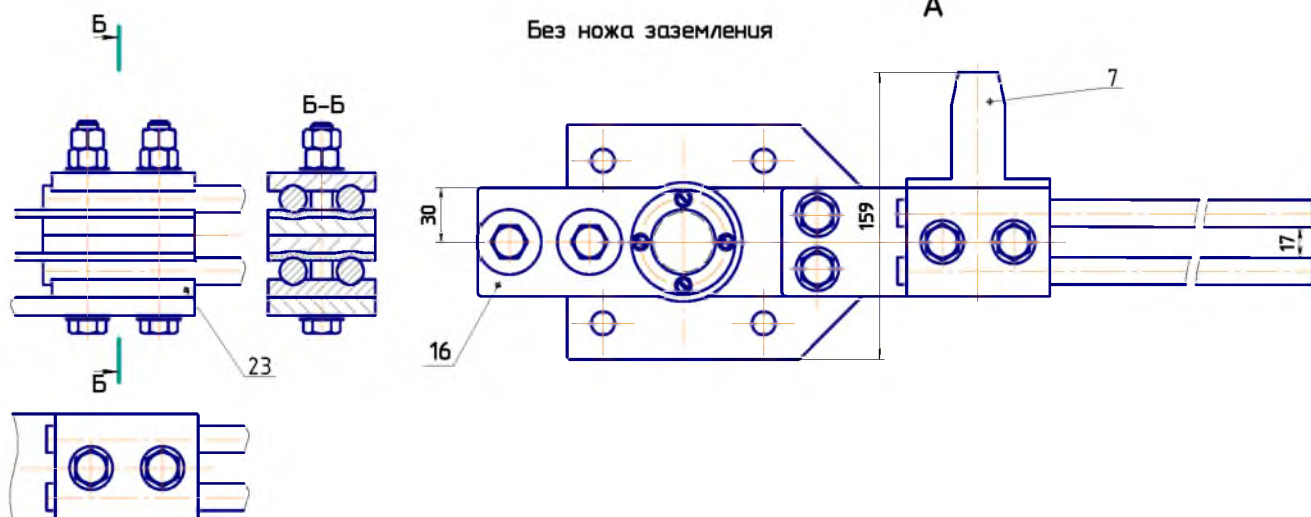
Подвижный нож контактный разъединителя РГП СЭЦ®-35/1000
